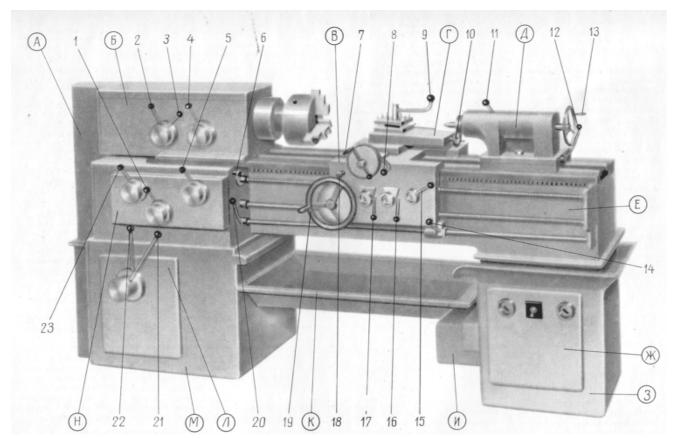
Обший вид токарно-винторезного станка модели 1А616
